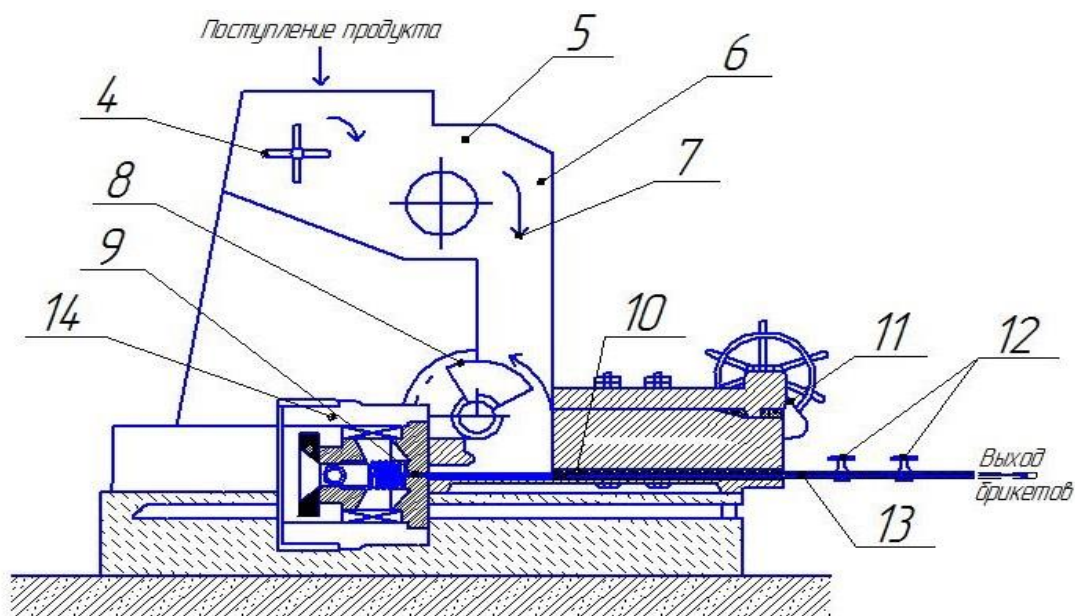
Схема штокового пресса с приводом от ЛЭМД. (1 – маховик; 2 – зубчатая передача; 3 – коленчатый вал; 4 – разрыхлитель; 5 – питающий механизм; 6 – питающий валик; 7 – канал; 8 – подпрессователь; 9 – шток-пуансон; 10 – прессовая камера; 11 – Механизм для регулирования брикета; 12 – нажимные механизмы; 13 – Мундштук; 14 – ЛЭМД).
